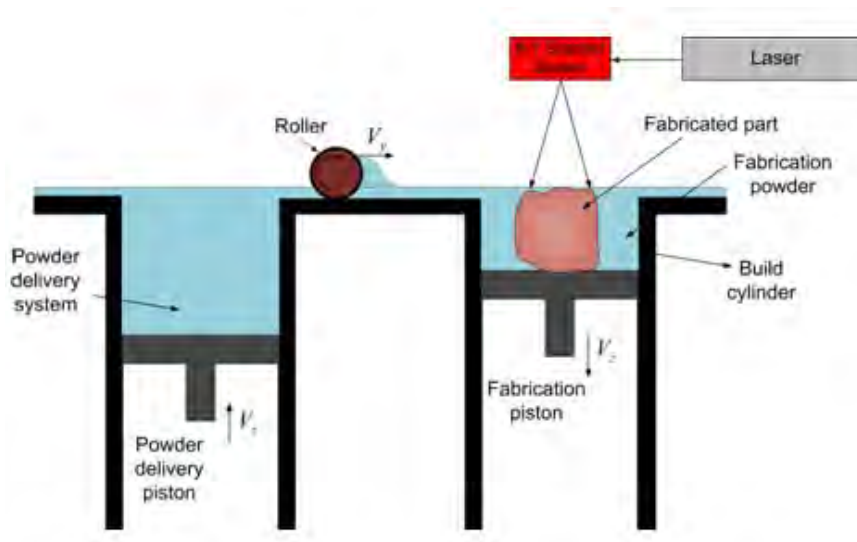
Schéma expliquant le principe de la technique de la fusion laser (30)
